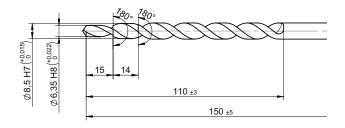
Stufenbohrer Typ 1337A für Montagenippel M10x1
